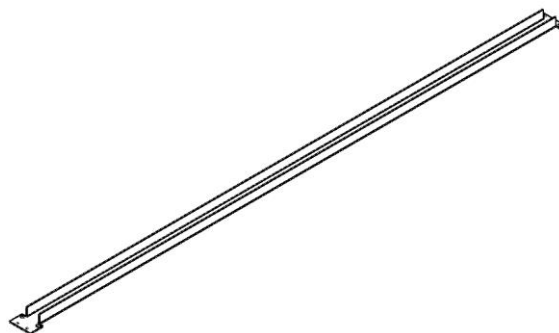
Perspectiva isométrica "Calha suporte 45mmx2m Carril VF".
